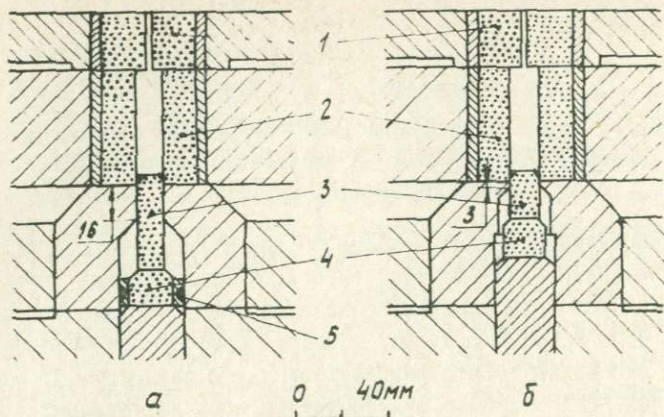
Твердосплавные детали одноступенчатого аппарата. Первоначальный (а) и улучшенный (б) варианты. 1 - крышка цилиндра, 2 - цилиндр, 3 - рабочий шток, 4 - пята, 5 - центрирующее кольцо.
